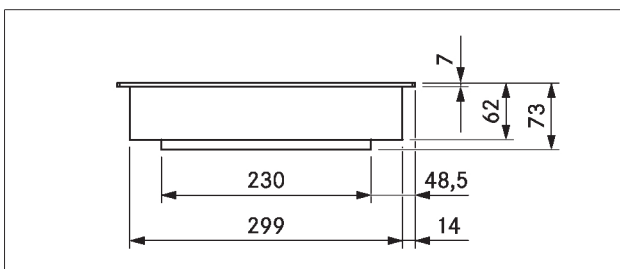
Dimensões do aparelho CKT, vista frontal
